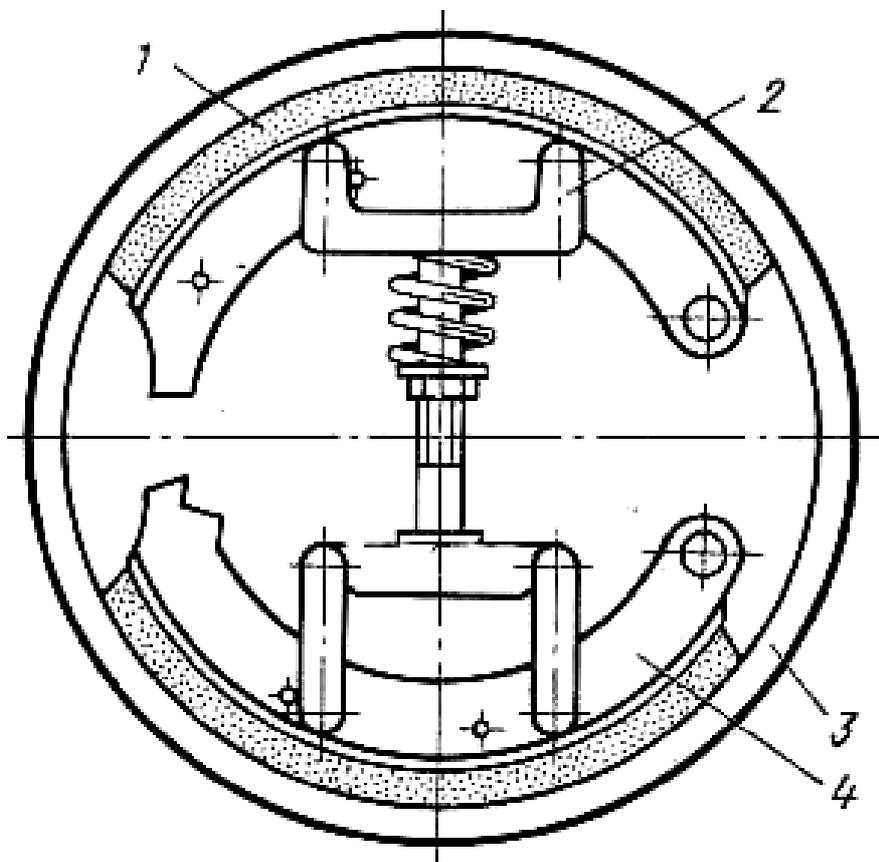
Приспособление для прессования тормозной накладки:
